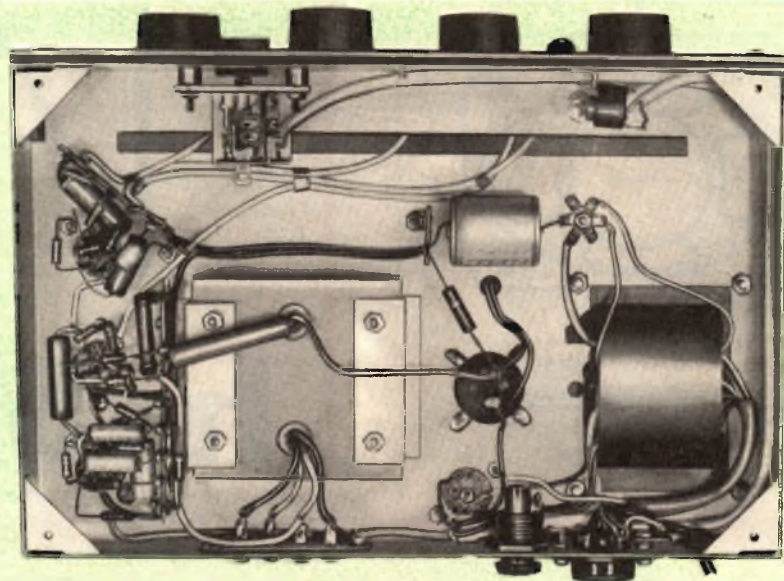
Telaio principale visto dal lato dei collegamenti.
